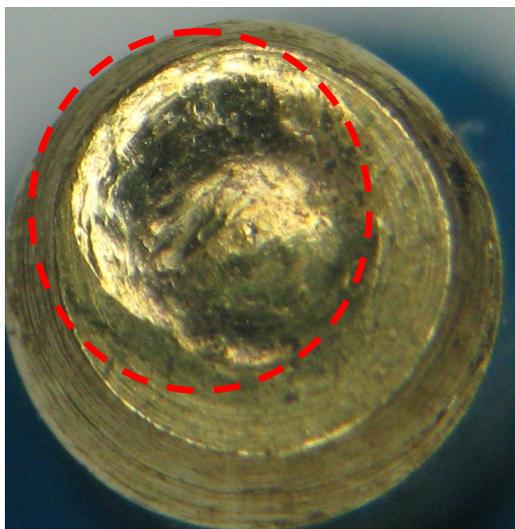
След на вершине одного из штифтов цилиндра в месте его контакта со штифтом корпуса
